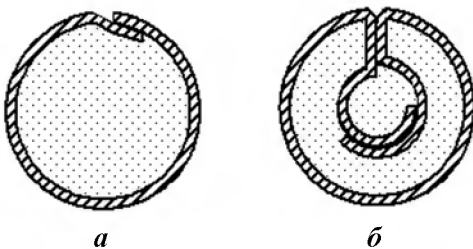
Загальний вигляд перерізу порошкових зварювальних дротів:
